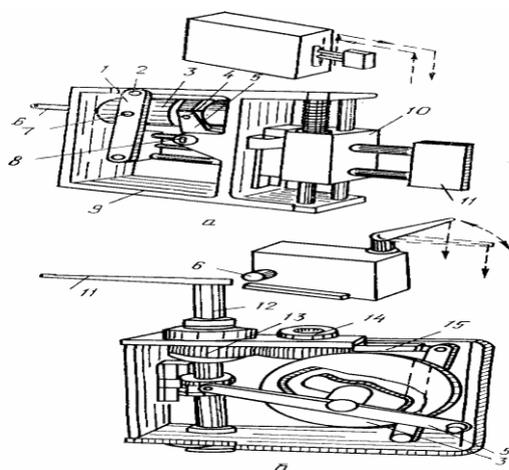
Сборочные головки фирмы Ferguson: а — с линейными движениями исполнительного устройства; б — с поворотом устанавливаемой детали
